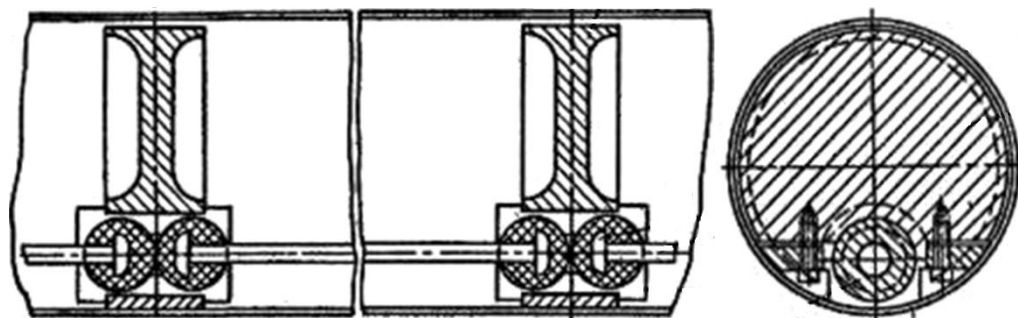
Шарнірний трубчатий скребковий конвеєр
